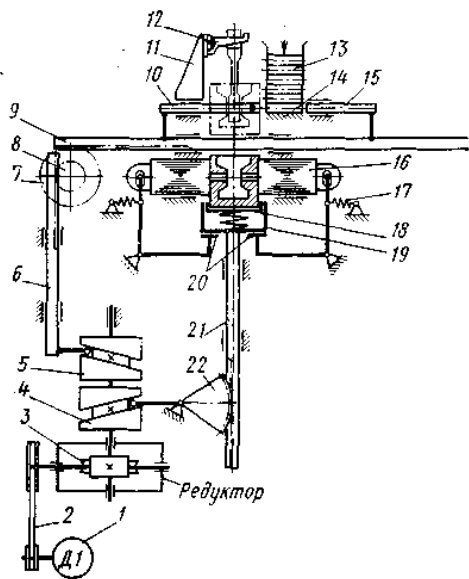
Кинематическая схема полуавтомата для сборки поршня с пальцем
